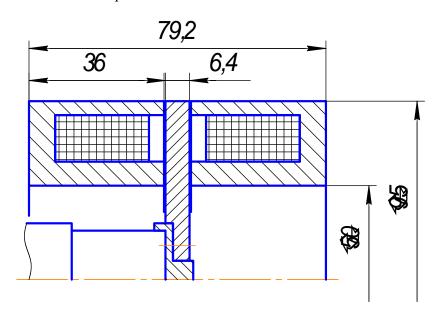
Габаритные размеры осевого электромагнитного подшипника
